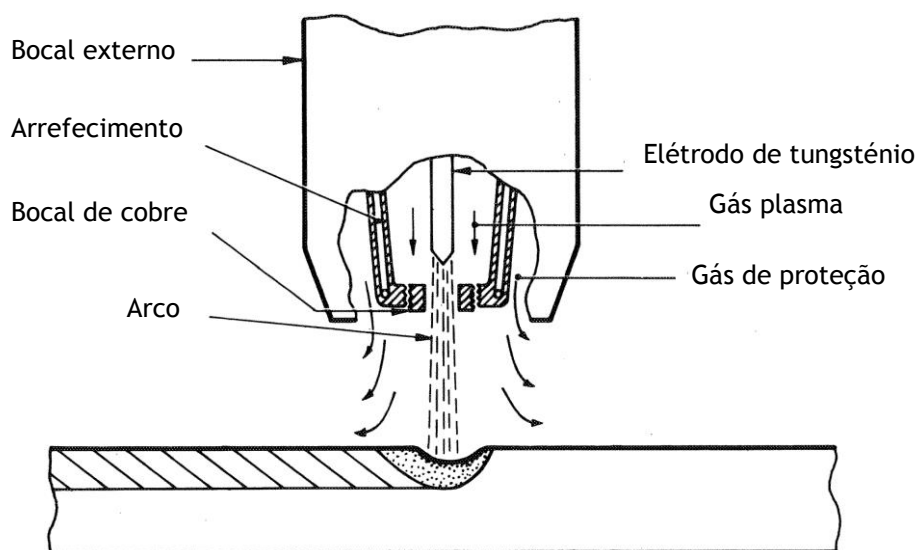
Configuração de uma tocha de soldadura por plasma
